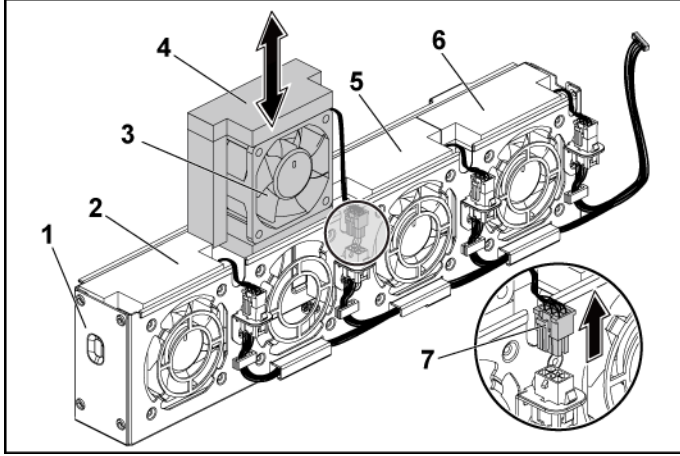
Bir Soğutma Fanı Kafesinin Çıkarılması ve Takılması
